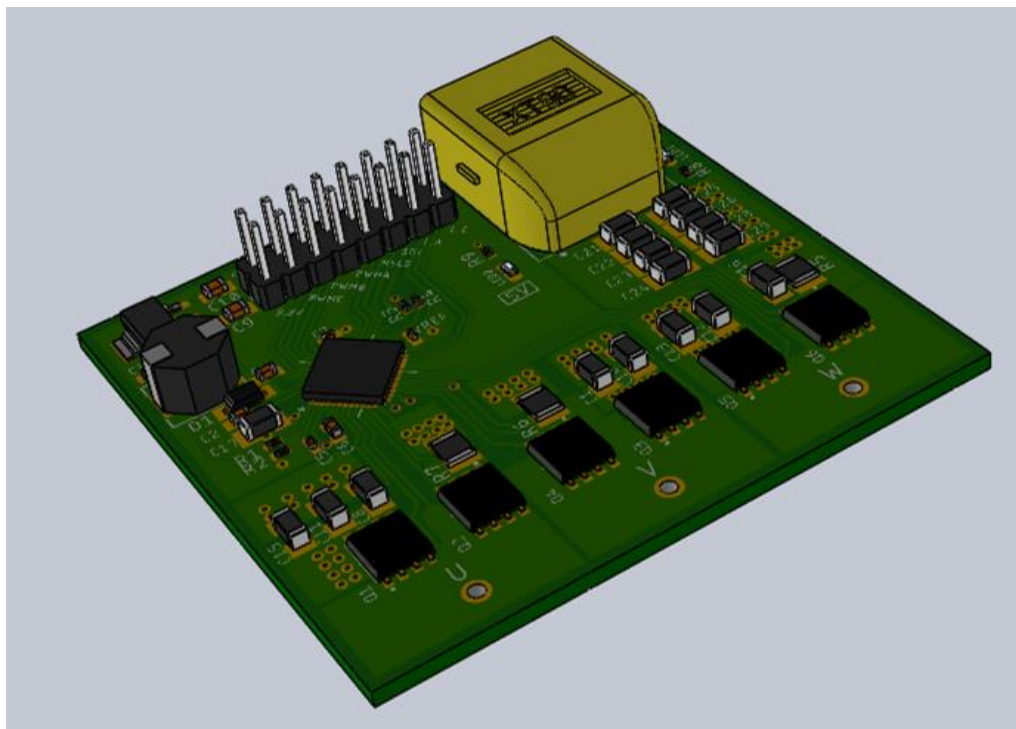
Model 3D de la PCB (Font: Ernest Porqueras)
